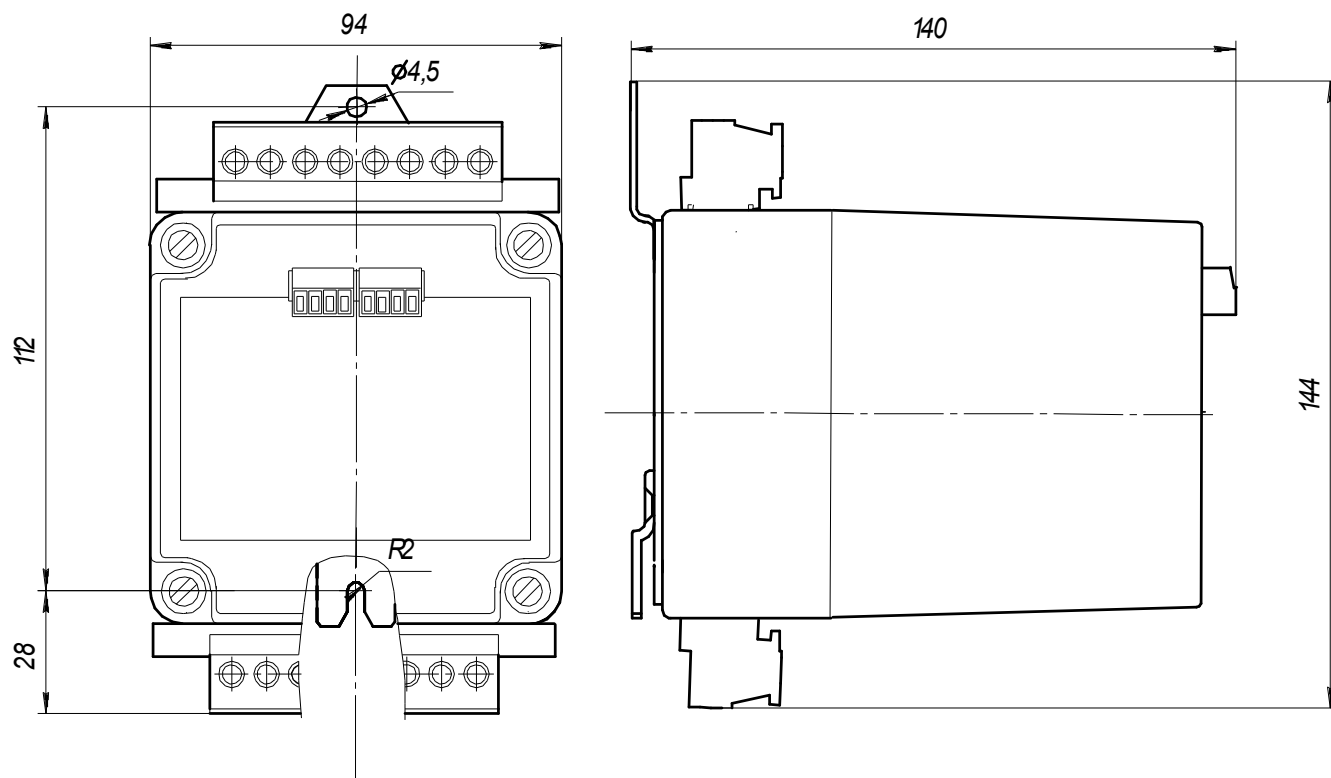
Габаритные и присоединительные размеры ПИ849Ц/XX-0
